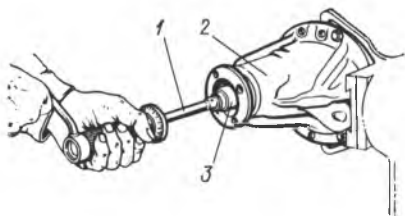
Проверка предварительного натяга подшипников ведущей шестерни:
